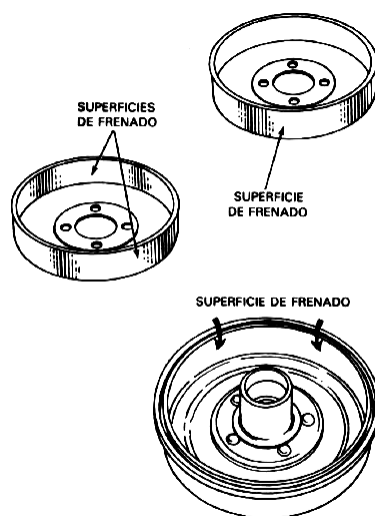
Vista del tambor de frenos (FMC Corporation)
